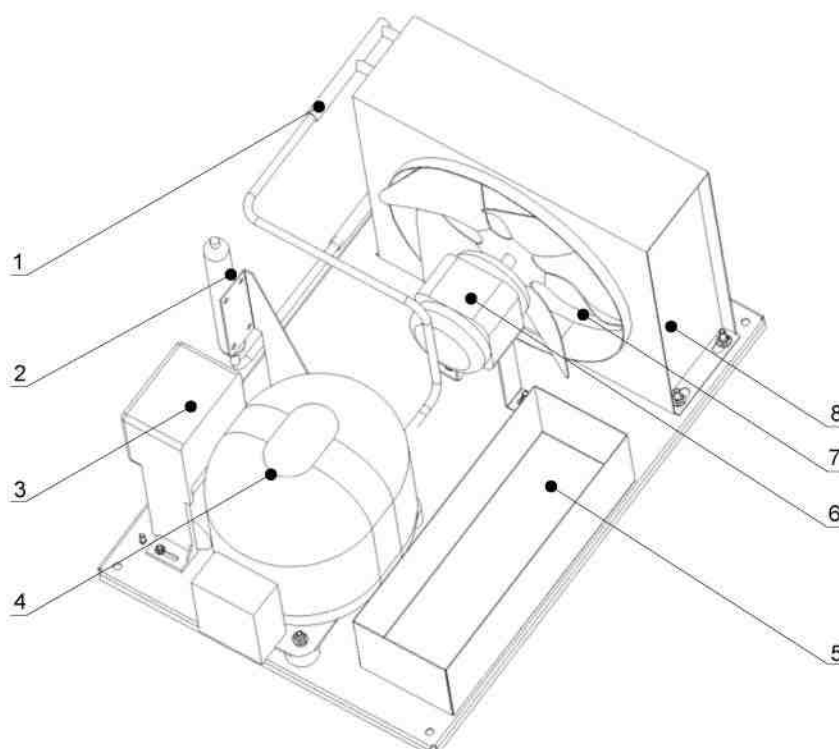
Холодильний агрегат: 1 – магістраль; 2 – фільтр осушувальний; 3 – блок пускового реле; 4 – компресор; 5 – кювета; 6 – мотор; 7 – крильчатка; 8 – конденсатор
